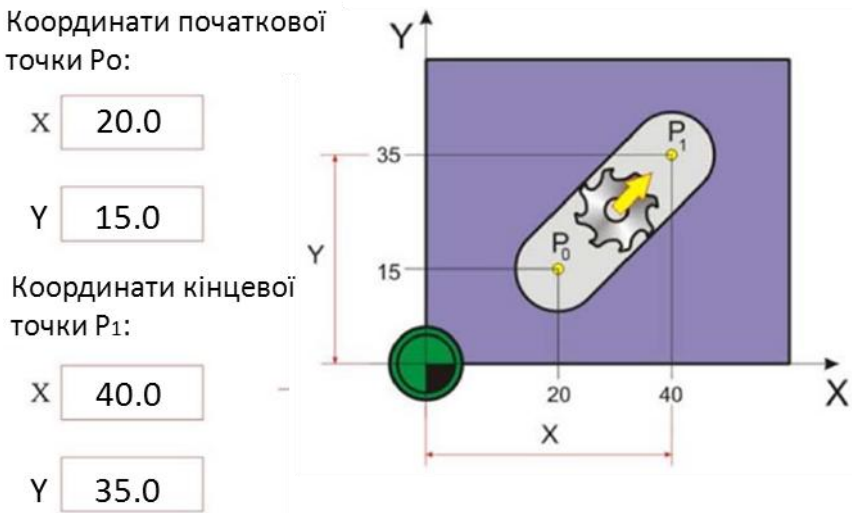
Основні точки фрезерних верстатів із ЧПК
